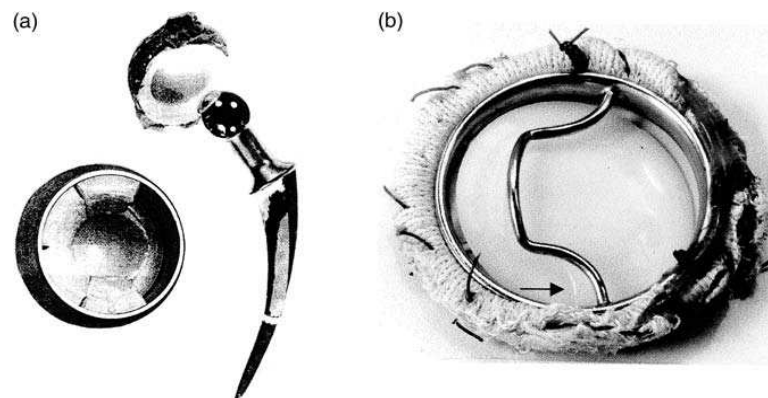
Exemples de fracture de fatigue : a-dans les implants de la prothèse de hanche
